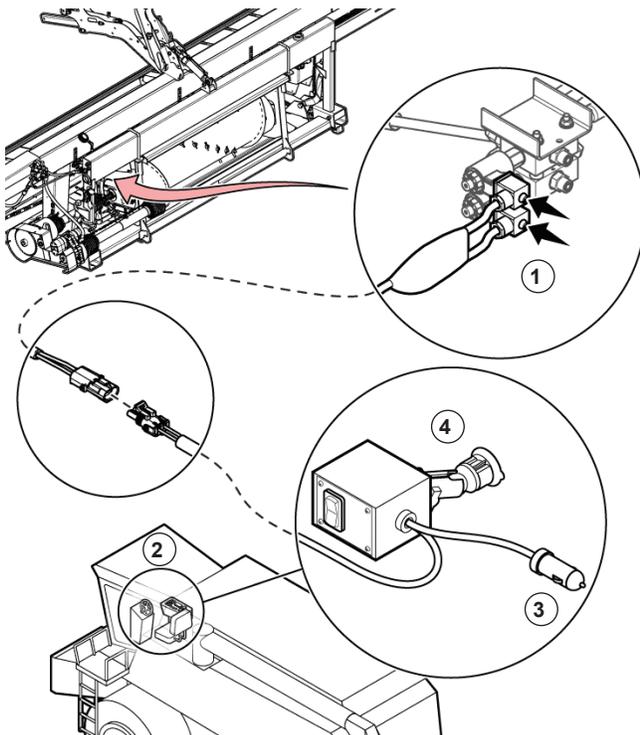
Installer le boîtier de sélection d'inclinaison hydraulique
